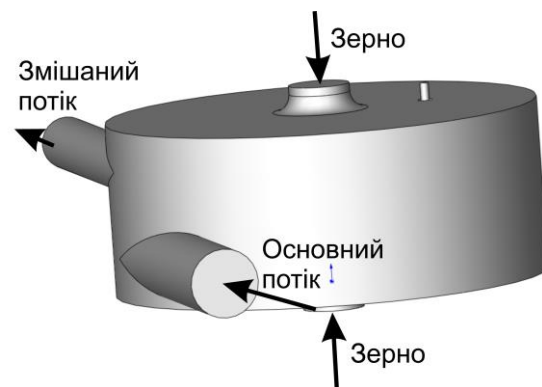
Розрахункова схема вихорокамерного нагнітача зерна
